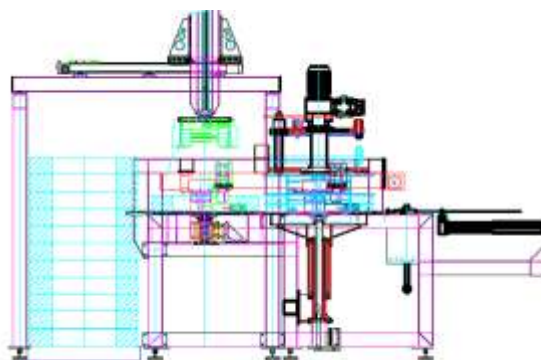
Imagen 3D máquina bobinadora empaquetadora
